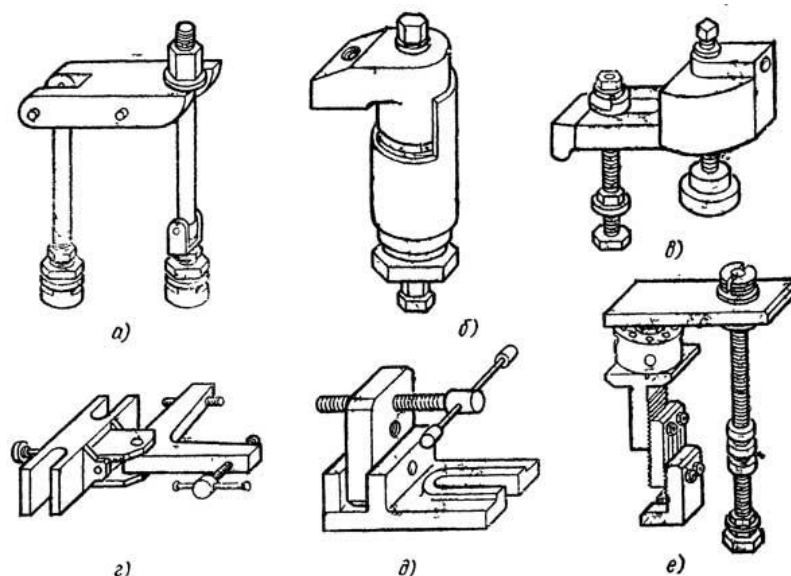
приспособления для фрезерования с ЧПУ
